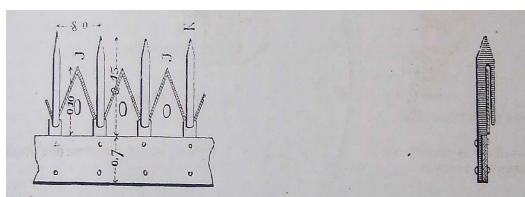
Barre de coupe de la machine Drey et doigt de profil
